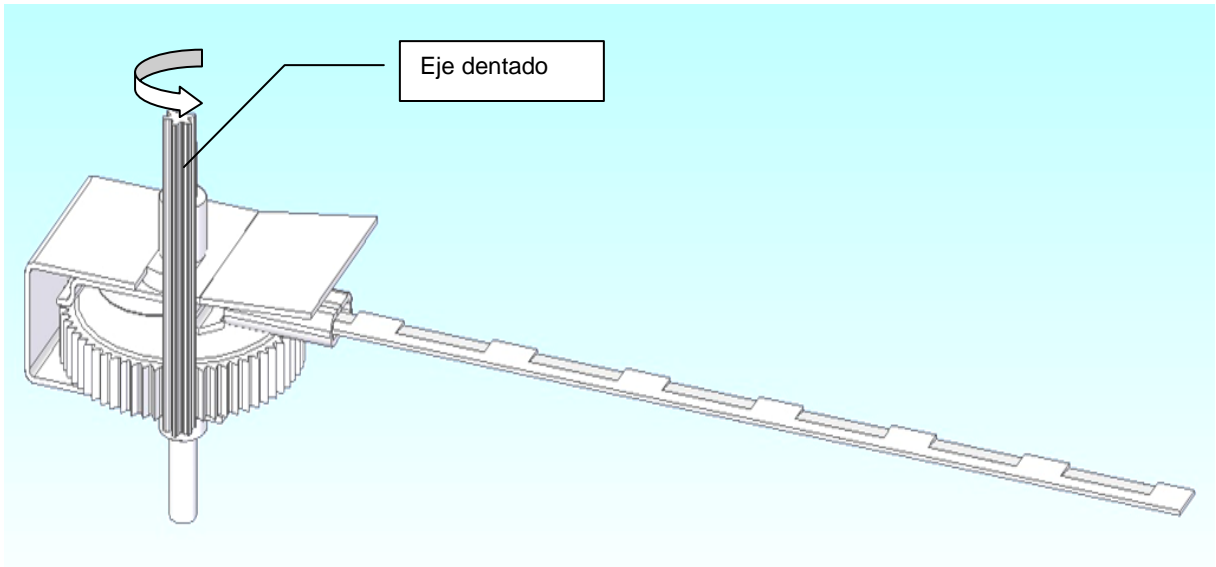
, Ensamble del mecanismo de corte oscilante.
